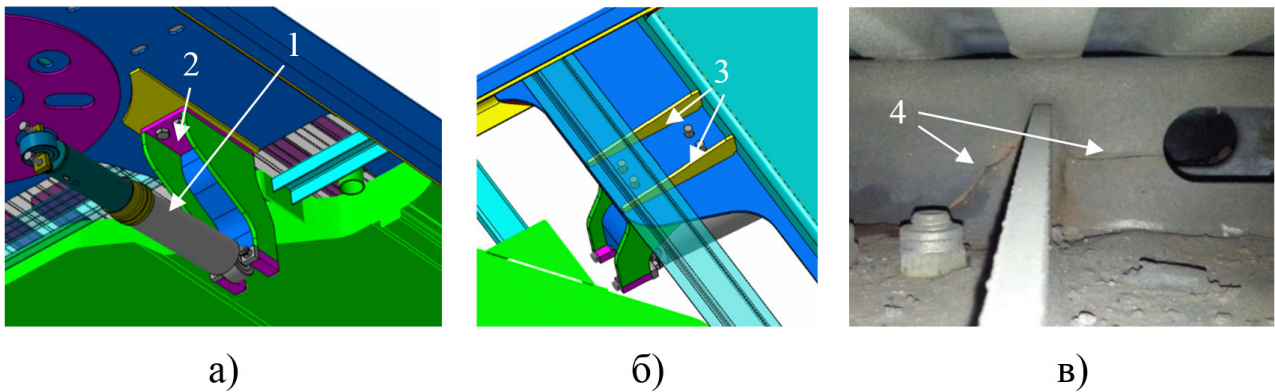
Вузол демпфера коливань виляння: а) вид зі сторони демпфера; б) вид зверху; в) тріщина бокової стінки шворневої балки.
